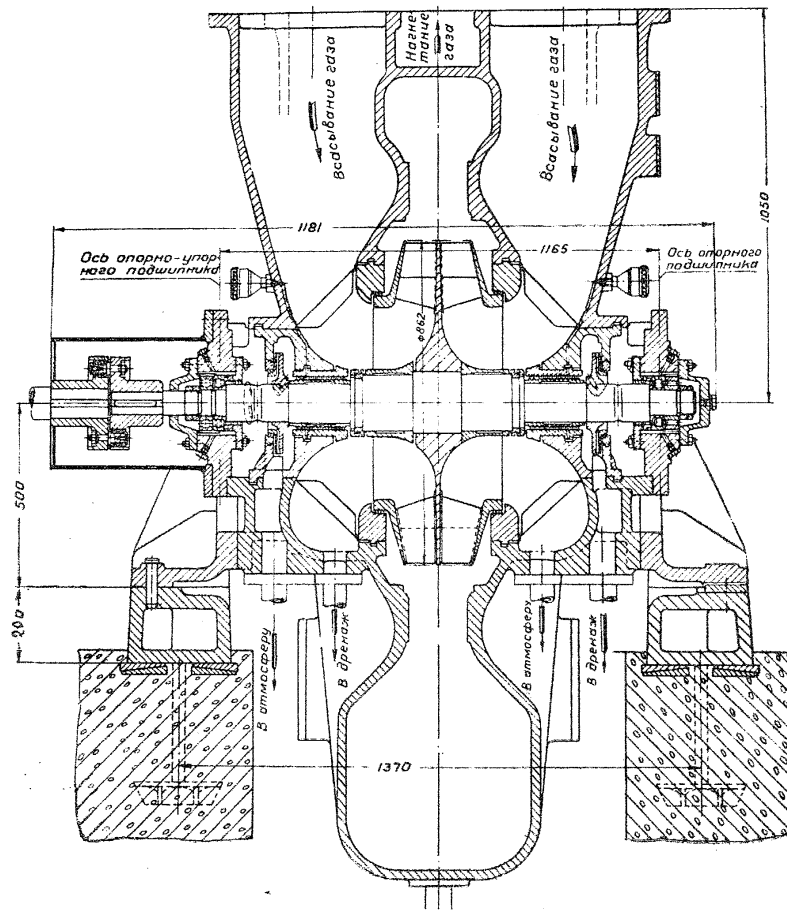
а. Типичный центробежный компрессор с небольшим повышением давления. Может применяться как тягодутьевой компрессор (при больших размерах корпус сварной), в производстве цемента и пр.
